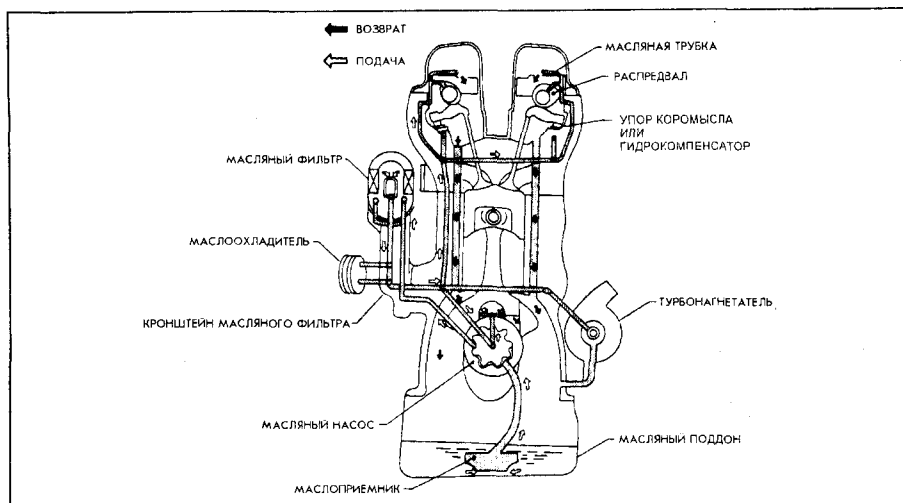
Схема смазки дизельного двигателя RD28Т.
